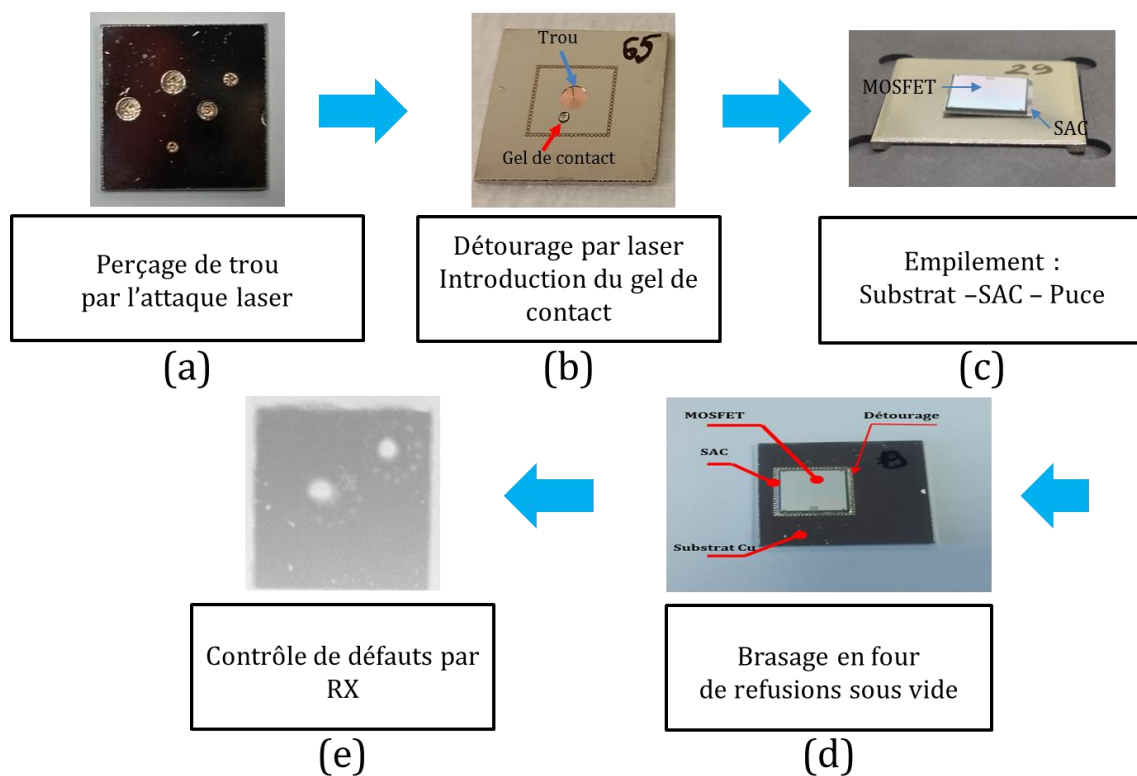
Procédé d'assemblage des prototypes MOSFETs
